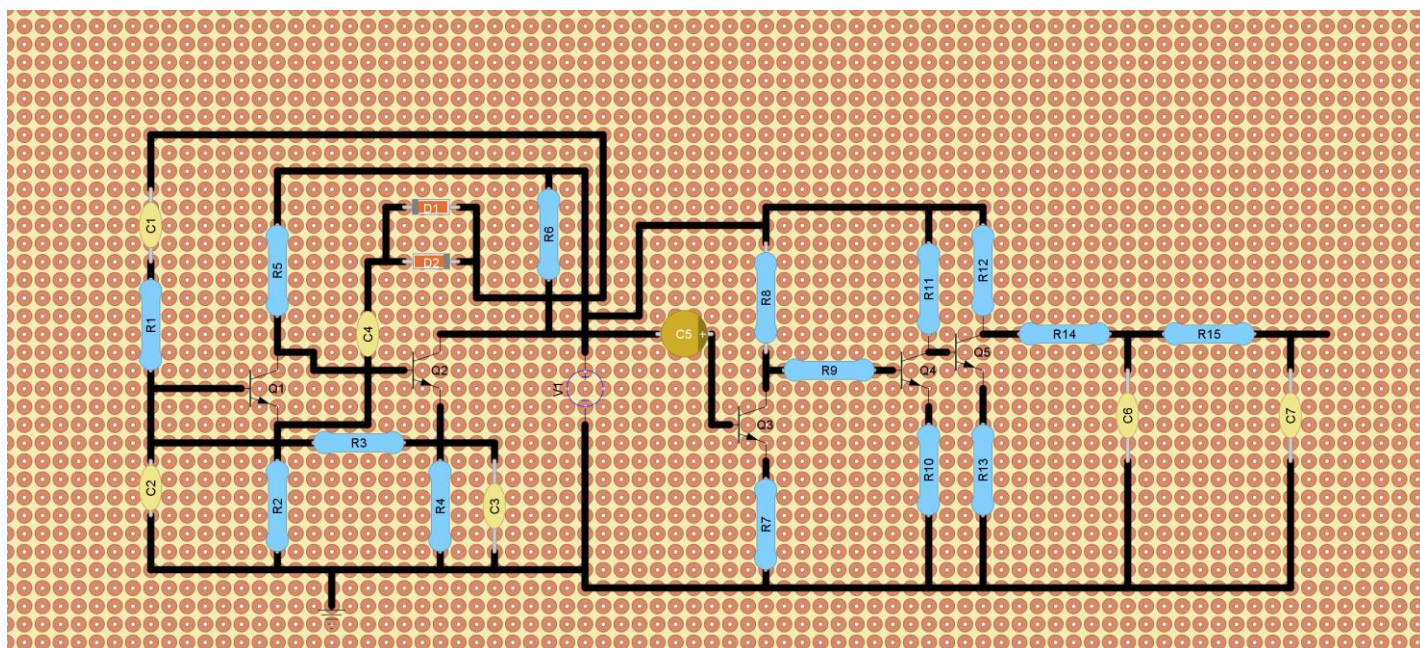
Planul de plantare al componentelor realizat în aplicația DIY Layout Creator
